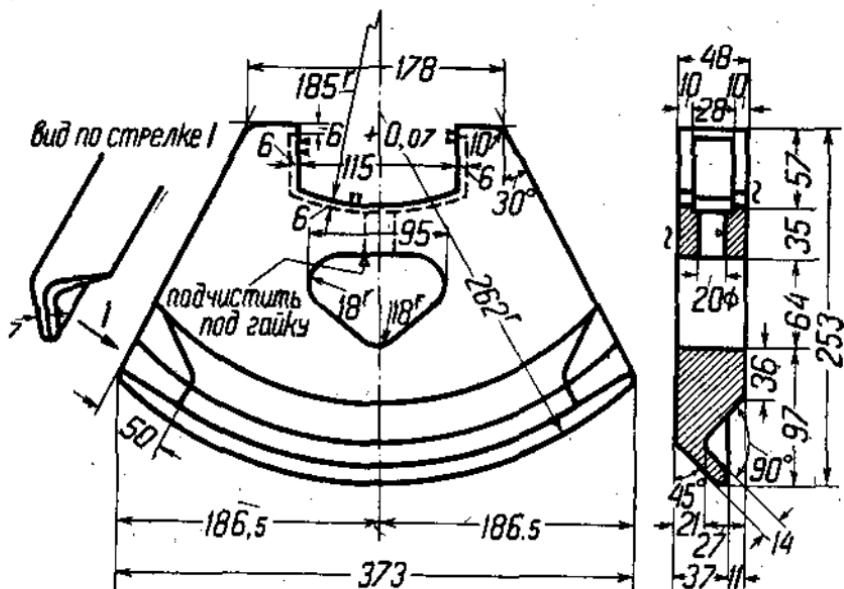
Противовес к коленчатому валу воздушного компрессора типа Бородино.
